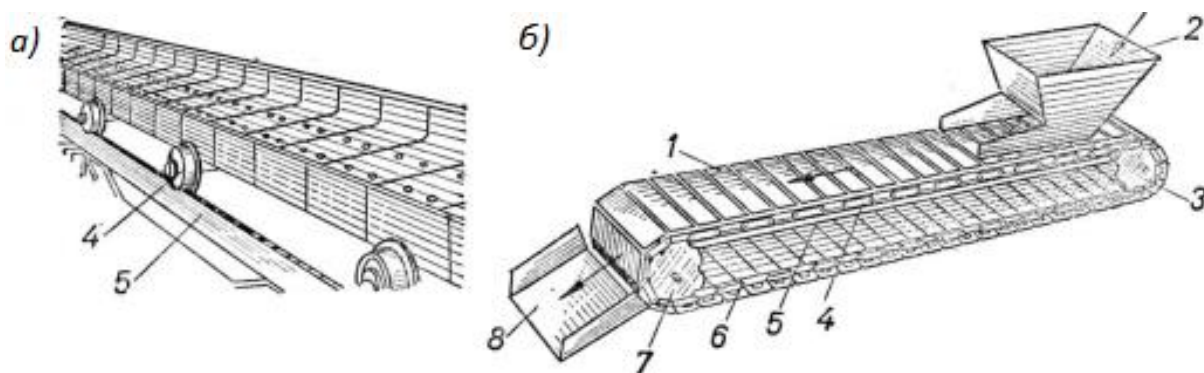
Пластинчатый конвейер-питатель: а – угловой; б – ленточный: 1 – пластины, прикрепленные к цепям; 2 – загрузочная воронка; 3 – натяжная звездочка; 4 – катки; 5 – неподвижные направляющие станины; 6 – бесконечные тяговые цепи; 7 – приводная звездочка; 8 – разгрузочный лоток
